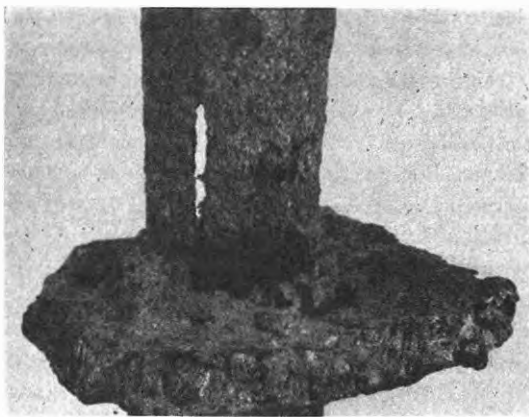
Corrosion électrochimique. Tube de fer soudé sur une tôle. La corrosion s'est portée sur la soudure. Agent corrosif : chlorure de butyle tertiaire
